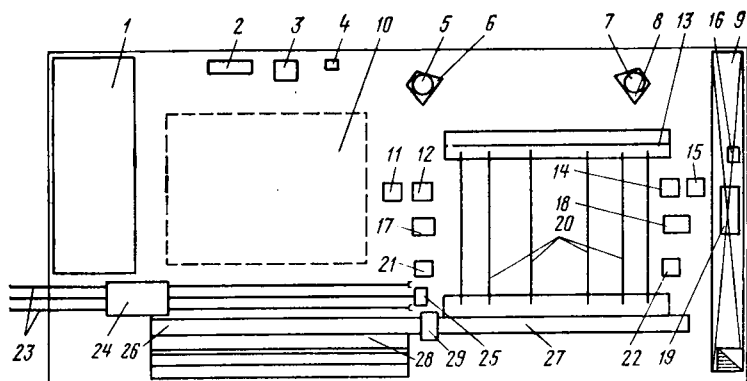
Схема расстановки оборудования и приспособлений технологической линии по обработке стальных труб и изготовлению трубных заготовок
